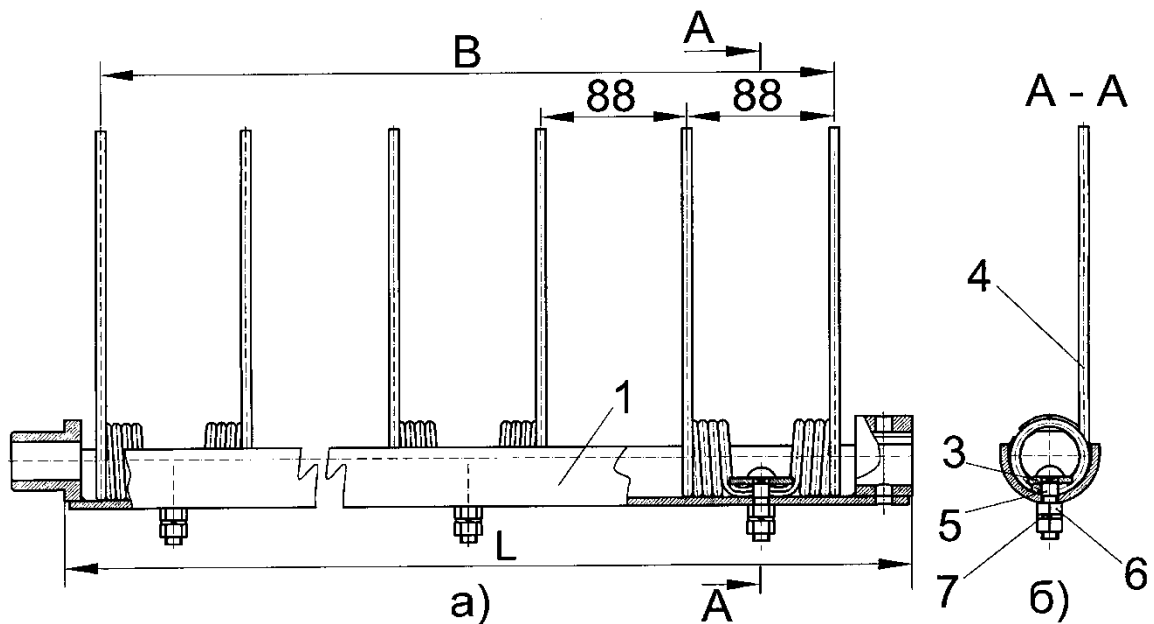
Конструкция унифицированной граблины ПМ в сборе с пружинными зубьями: а) – общий вид граблины; б) – вид на граблину по сечению А–А; 1 – держатель зубьев; 3 – шайба зуба; 4 – зуб пружинный; 5 – болт М10х40. 58.019 ГОСТ 7802-81; 6 – гайка М10-6Н.5.019 ГОСТ 5915 – 70 (2 шт.); 7 – шайба 10Т.65Г.019 ГОСТ 6402-70.
